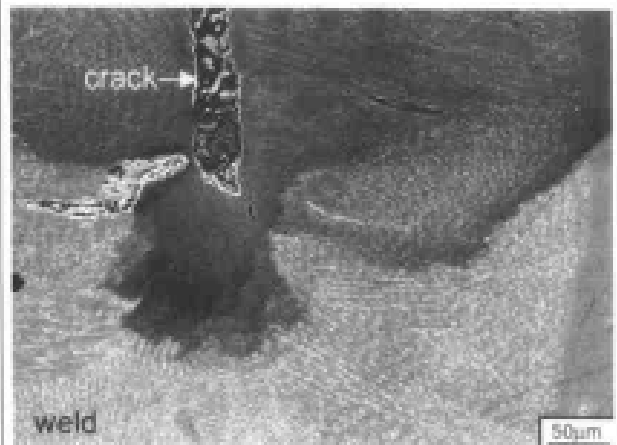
激光焊接, 42CrMo 合金/42CrMo 合金, CO<sub>2</sub> 激光, 焊缝底部, 功率 2800W, 焊接速度 1.75m/min
